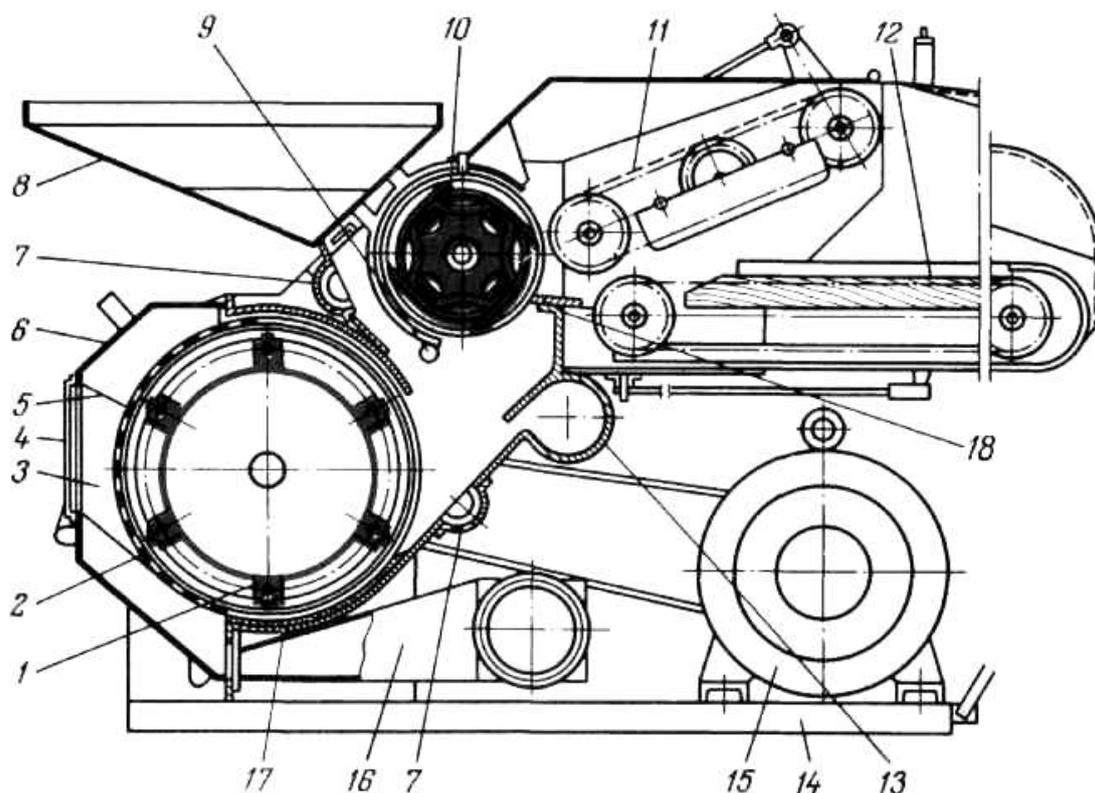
Схема дробилки КДУ-2 (разрез):
